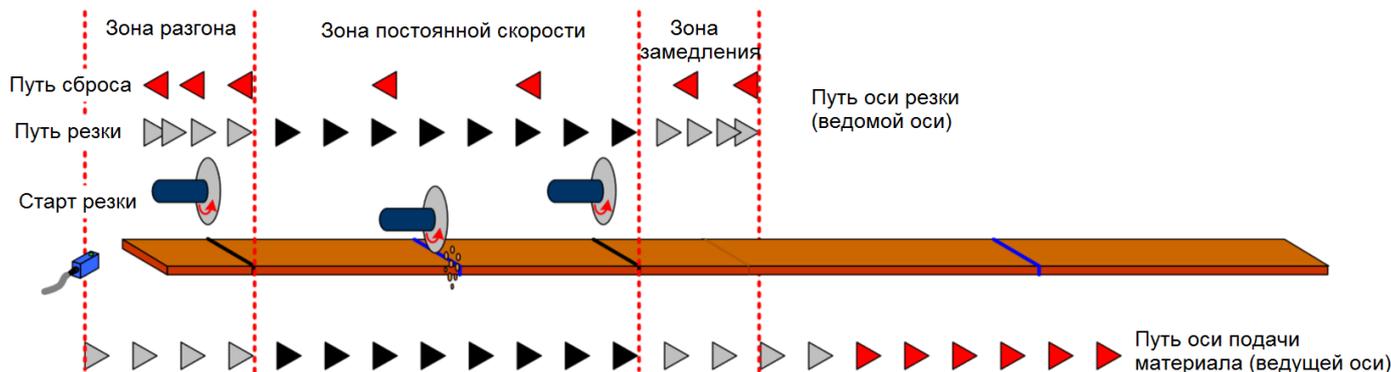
Траектория резки и рабочий цикл режущего станка
